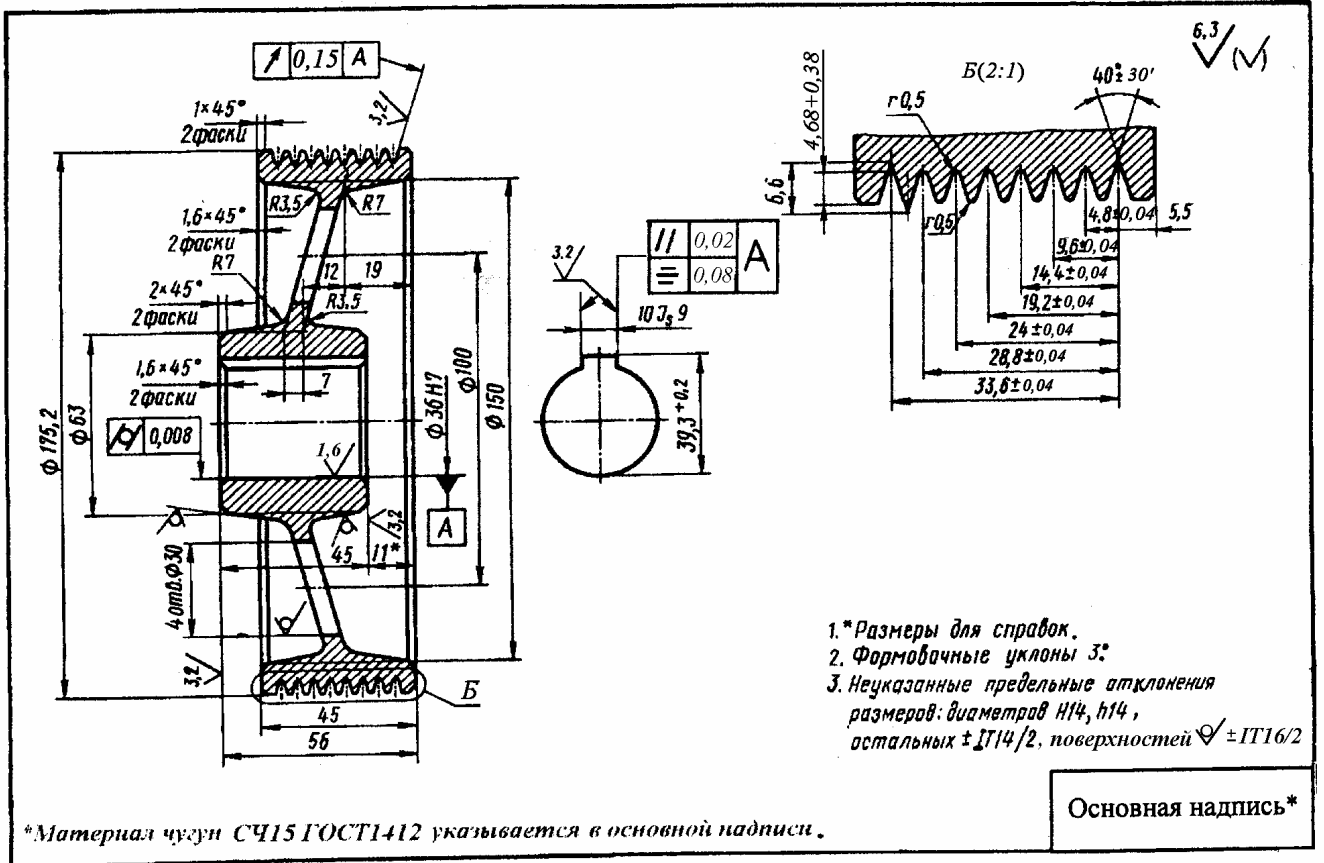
Рабочий чертеж шкива для поликлинового ремня
